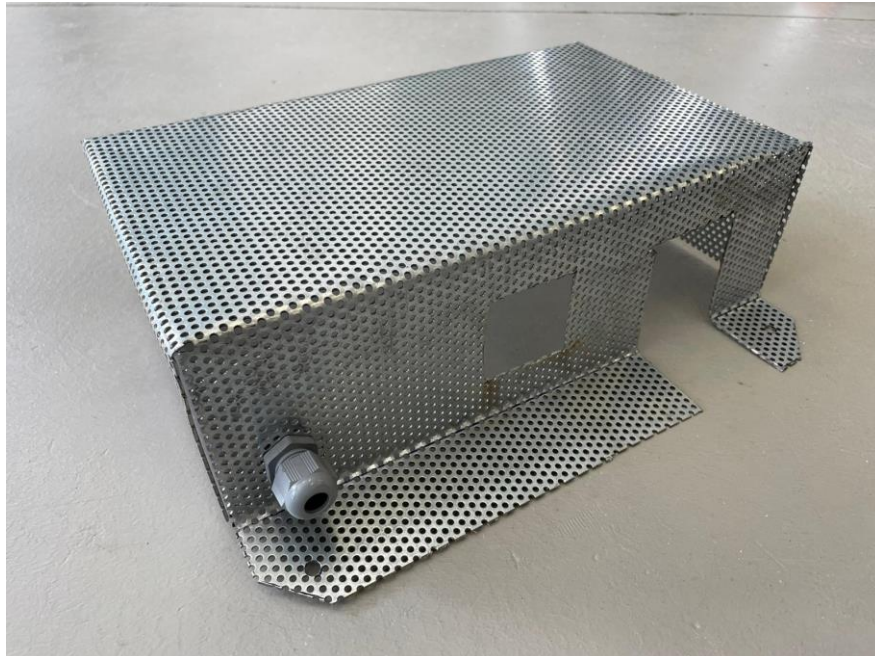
Cubierta para cajetín eléctrico (vista inferior)
